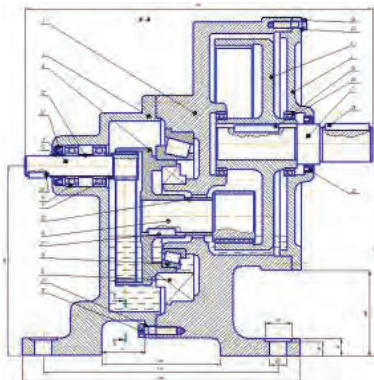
Редуктор с расположением опор быстроходного колеса в одной плоскости
